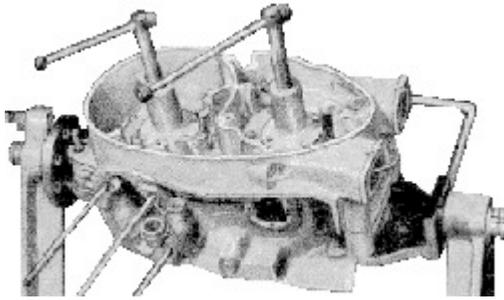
Trennschrauben zum Auseinanderdrücken des Gehäuses (Montagebock 05 MV 33-0)
